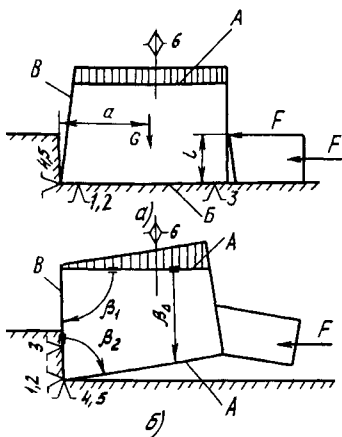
Смена баз у заготовки при закреплении ее в тисках
